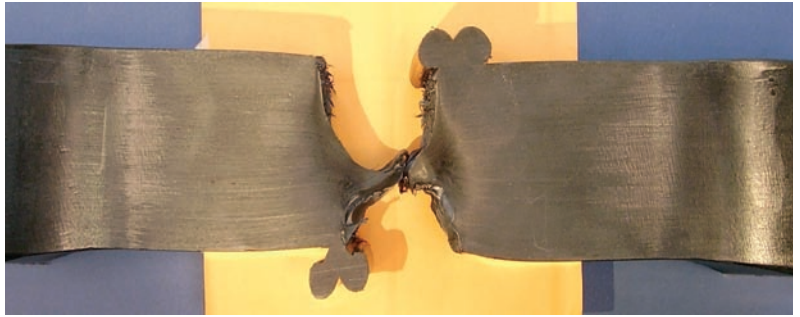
Heizelementstumpf-Schweißung aus PE 100-RC-Rohr (Wanddicke 58 mm) nach dem Zeitstandzugversuch mit Bruchverlauf außerhalb der Fügeebene
